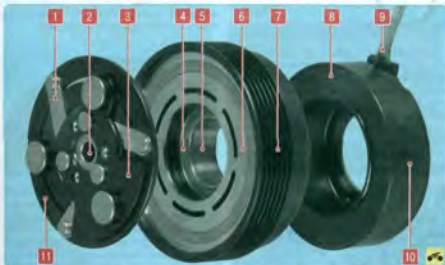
Электромагнитная муфта привода компрессора: 1 – упругий стальной проводок; 2 – шлицевое отверстие ступицы диска; 3 – ведомый диск муфты; 4 – подшипник; 5 – внутренняя обойма подшипника; 6 – рабочая поверхность шкива; 7 – рычаг шкива; 8 – обмотка электромагнита; 9 – жгут проводов электромагнита; 10 – корпус электромагнита; 11 – прижимной диск муфты
